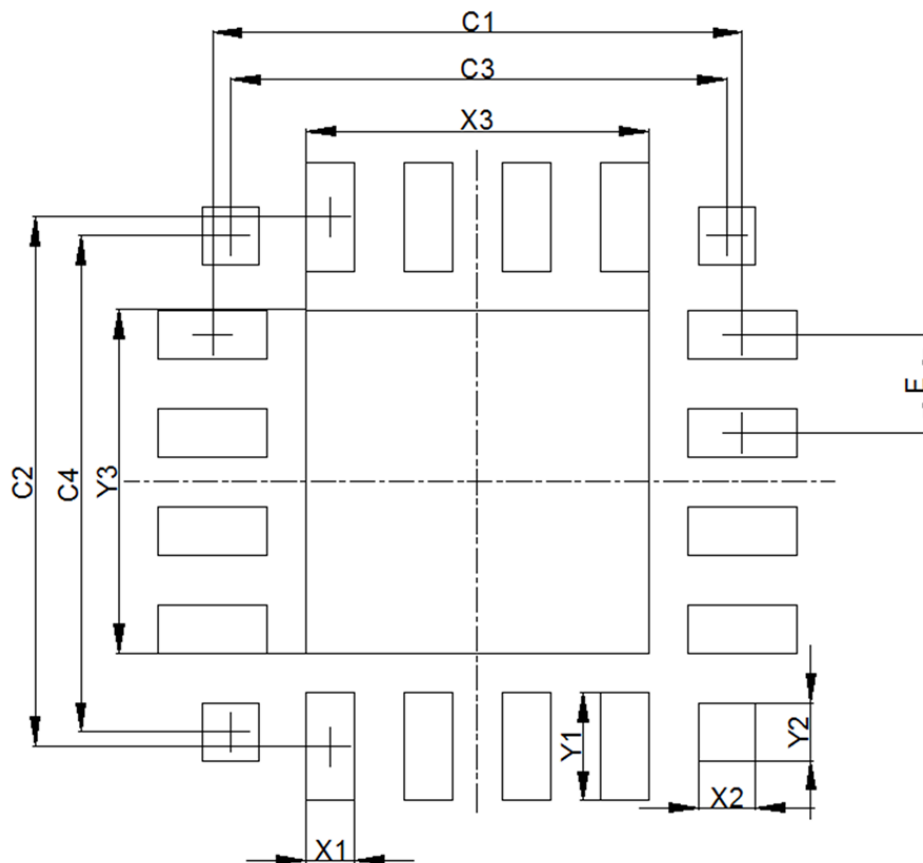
QFN20 PCB 焊盘布局图
